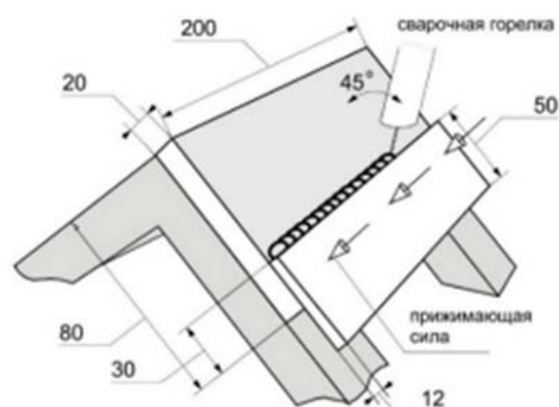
Схема сборки и сварки образца для определения склонности покрытия к порообразованию
